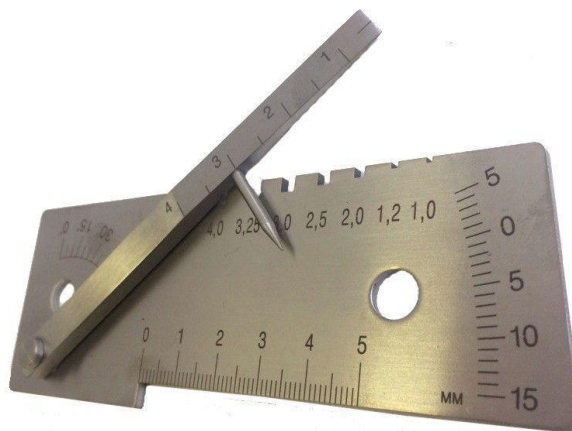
13 – Универсальный шаблон сварщика УШС.
